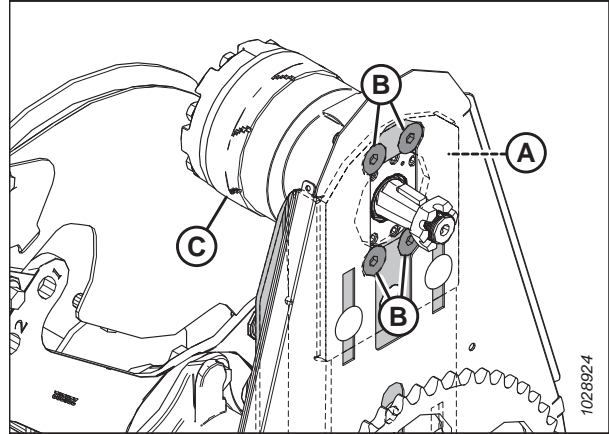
Parafusos de montagem do motor de acionamento do molinete
